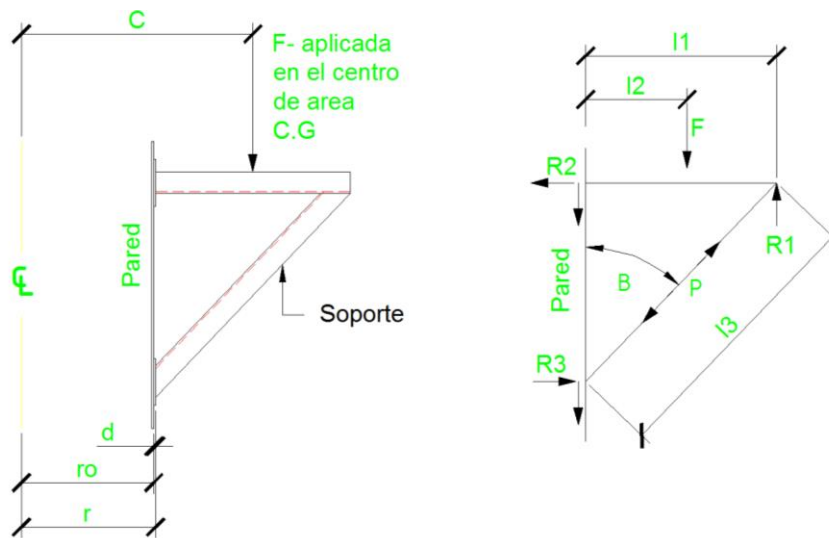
Dimensiones, fuerza, y reacciones para soporte
